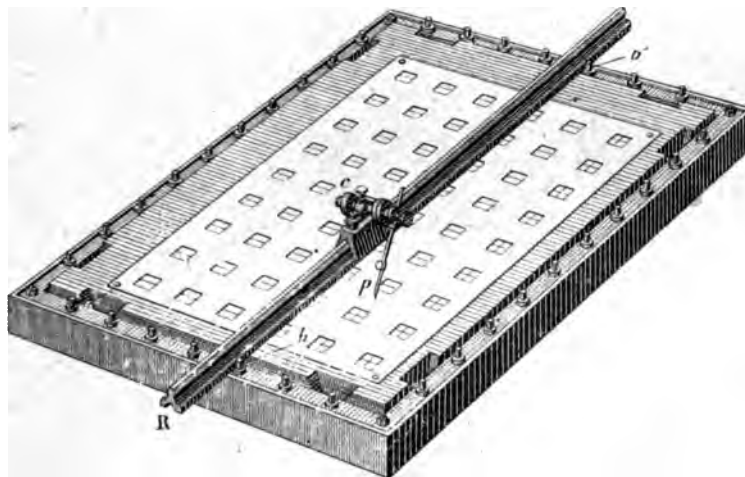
MACHINE SERVANT A QUADRILLER LES PLANCHES MATRICES.
